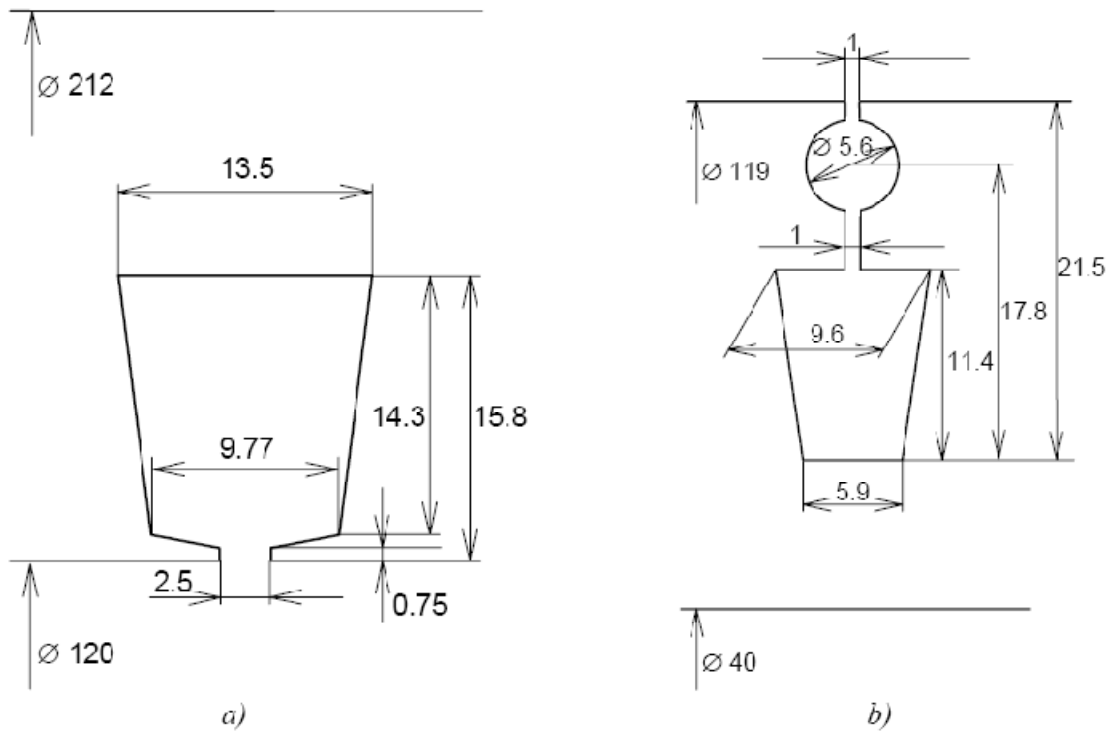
a) Ranura del estator, b) Ranura del rotor. Dimensiones en mm
